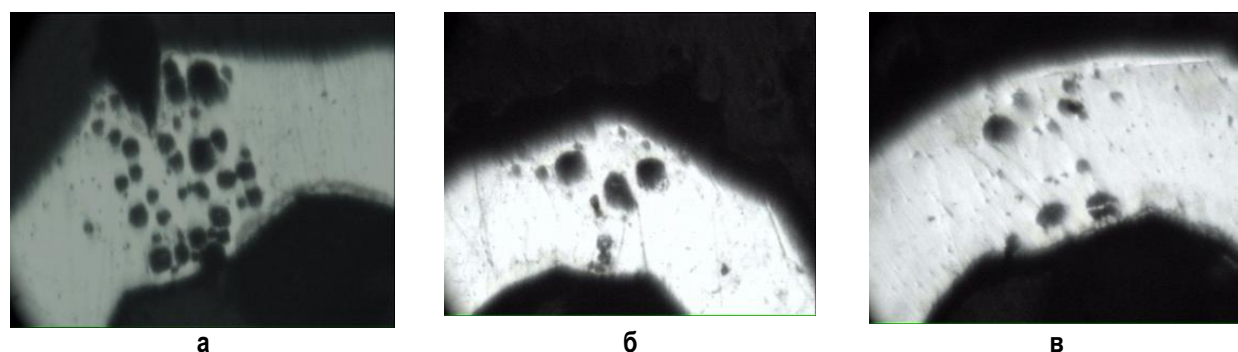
Внешний вид сварного соединения проволоки, отожженной с применением различных защитных сред (а – аргон, б – вакуум), и из сплава палладия (в), модифицированного титаном, $\times 120$
